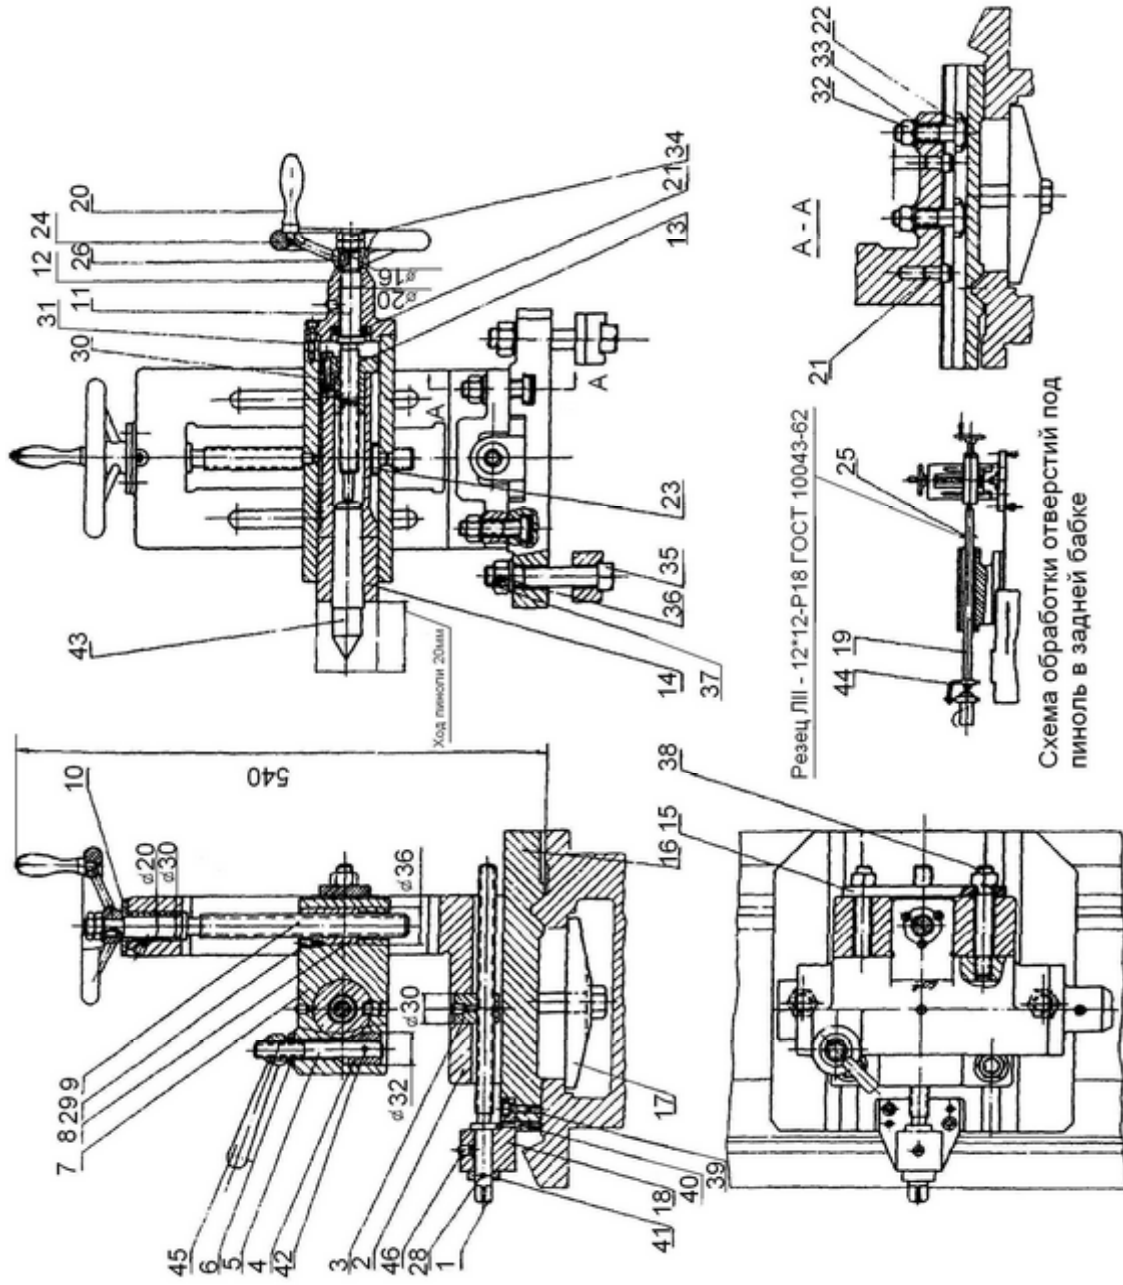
Приспособление для растачивания отверстий под пиноль в задней бабке СД 7111 – 4009
